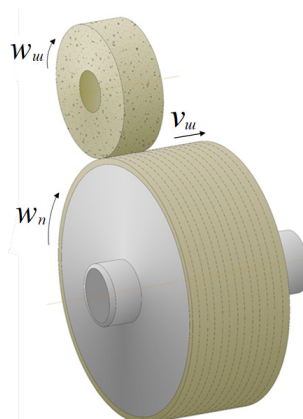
Предварительное шлифование пакета заготовок дисковых ножей
